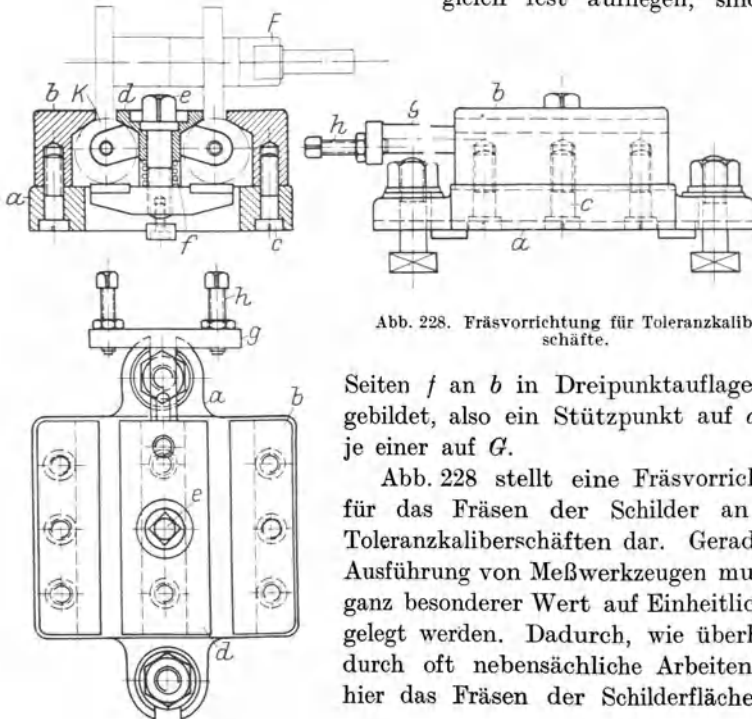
Fräsvorrichtung für Toleranzkaliberschäfte.
